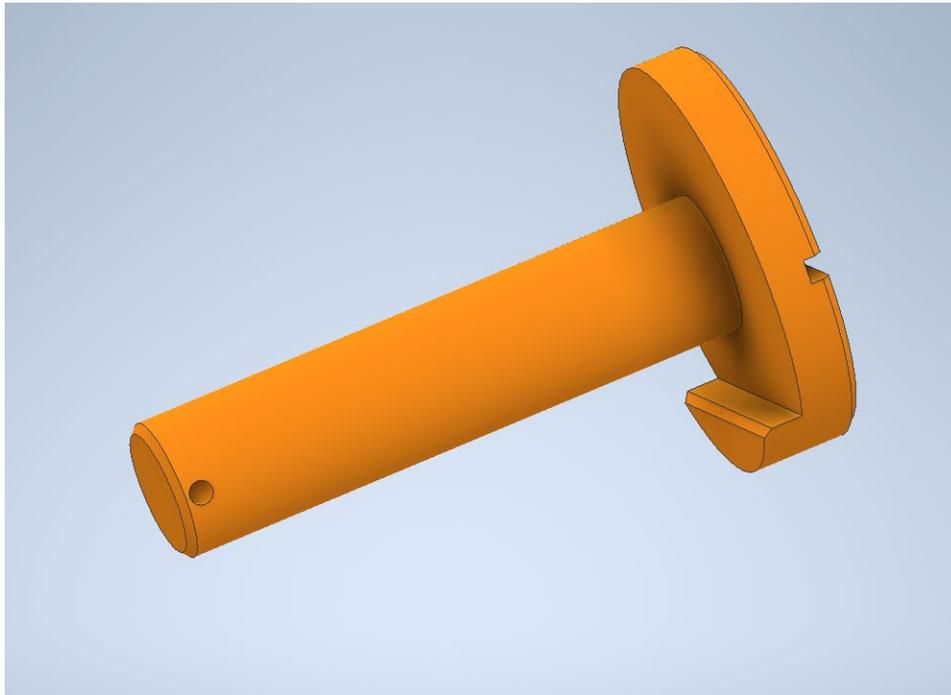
Общий вид детали №4 для импорта и подготовки чертежа.
